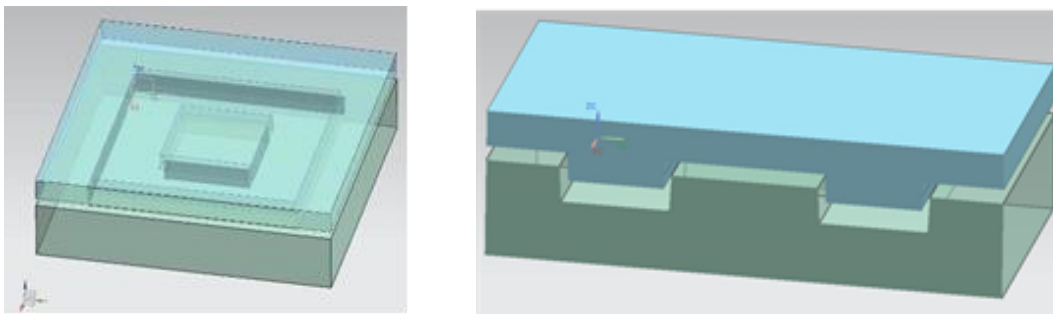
Vista isométrica (izquierda) y vista seccional (derecha) del molde conceptual.
